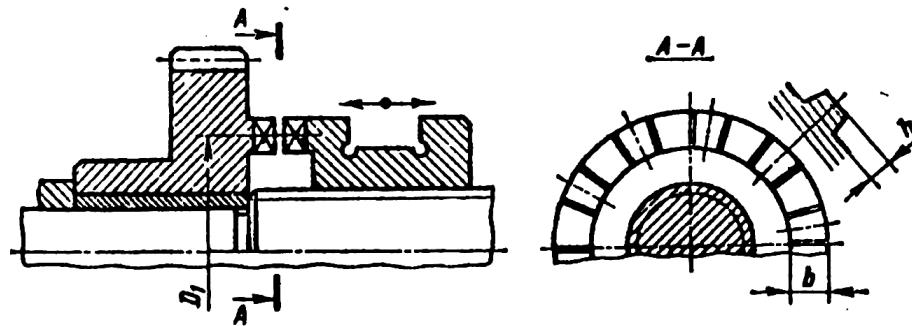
Принципова конструкційна схема кулачкової муфти
